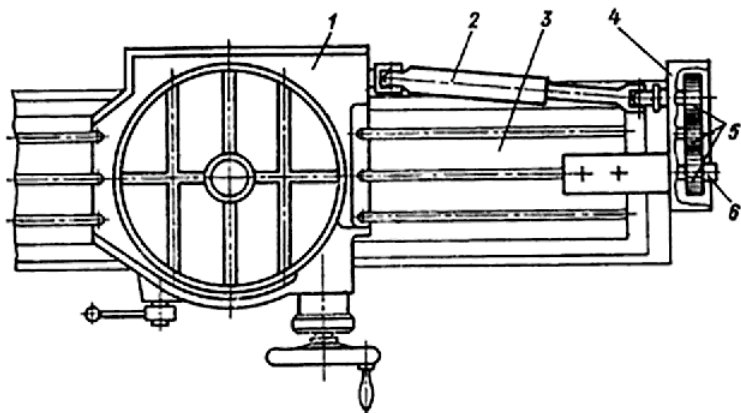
Круглый поворотный стол с приводом от механизма подачи фрезерного станка
